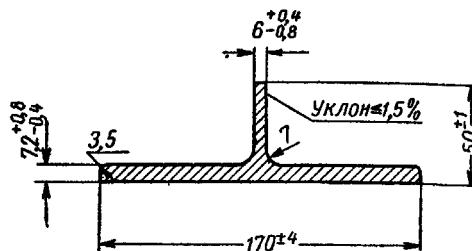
Размеры и допуски профиля для сварных двутавровых балок
